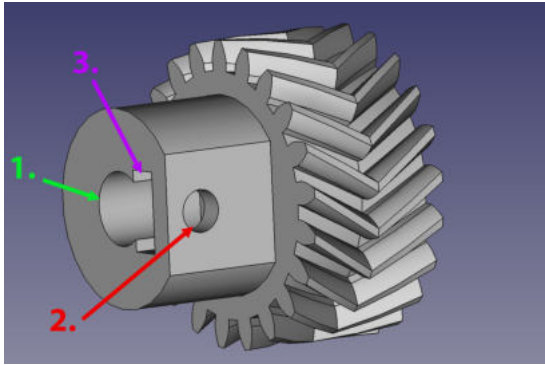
Zahnrad an Motor für Drehung der Kamerahalterung. Mittiges Loch für Motorpin (1.). Loch für Befestigung des Zahnrad an Motorpin (2.). Einschub für Mutter damit Schraube gegen Motorpin geschaubt werden kann (3.).
